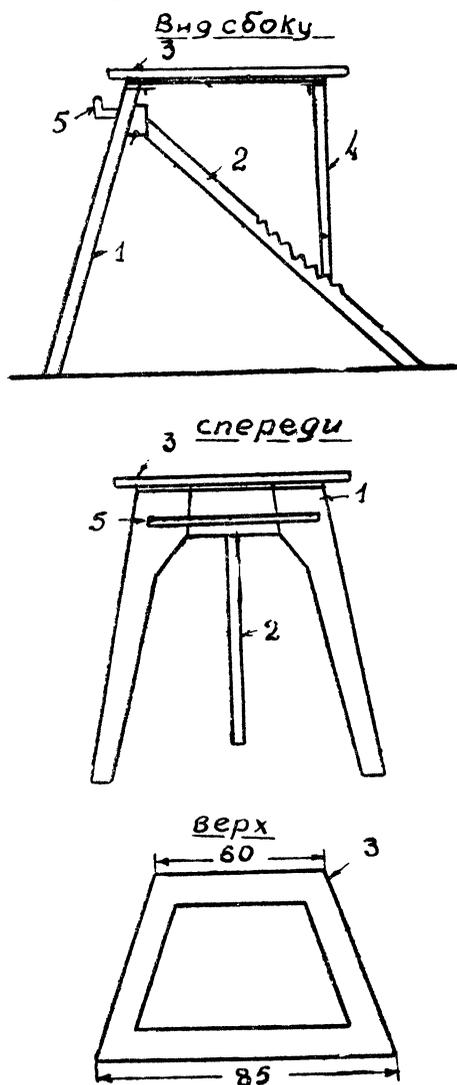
Чертежный стол. 1—передние ножки, 2—подставка, поддерживающая в определенном положении верхнюю доску, 3—верхняя доска, 4—задняя подвижная ножка, 5—полочка для инструментов.
